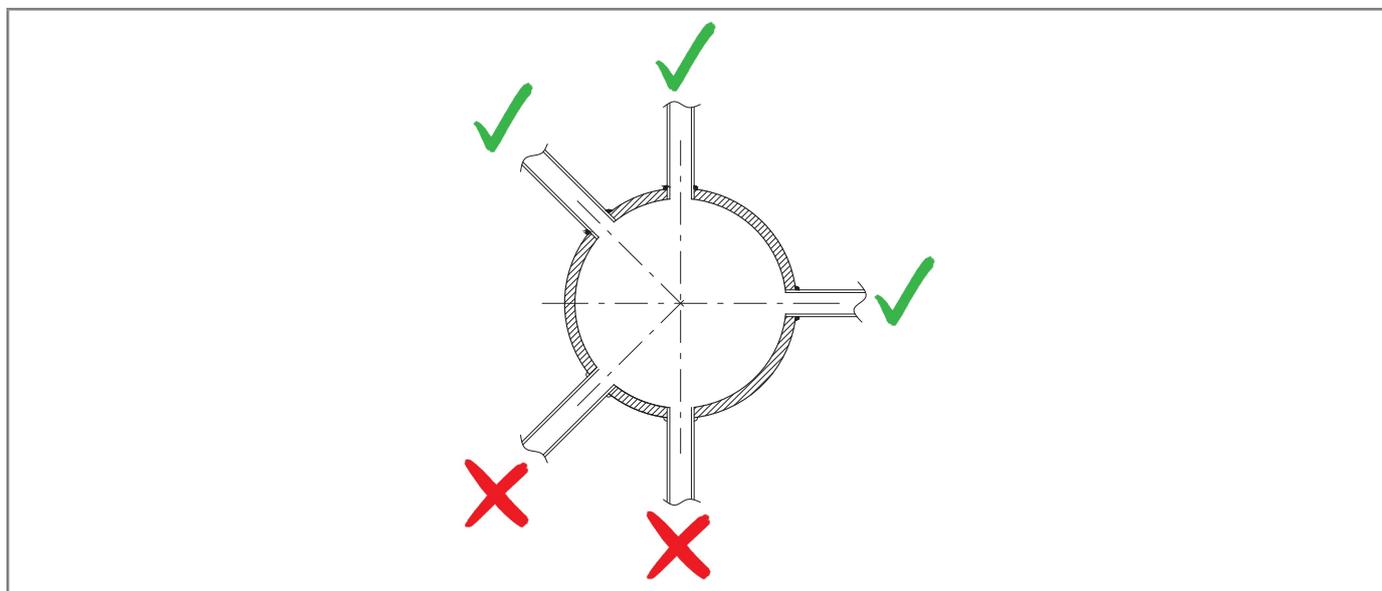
Geschweißte Anschlüsse der pneumatischen Verbindung
